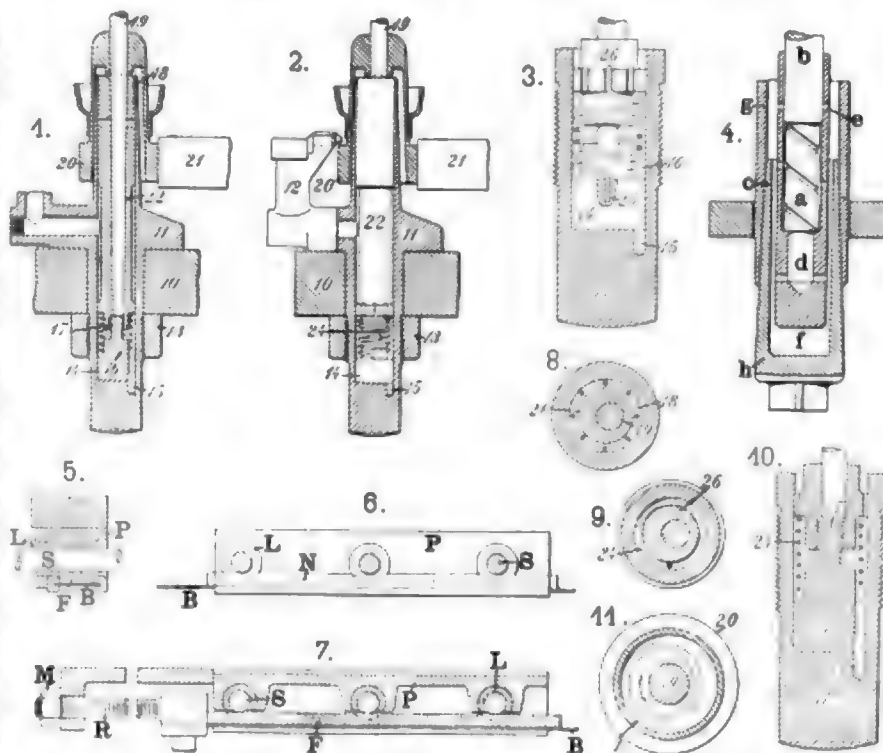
Z. A. Neue Spindel und Spindellagerungen für Spinn- und Zwirnmaschinen.
